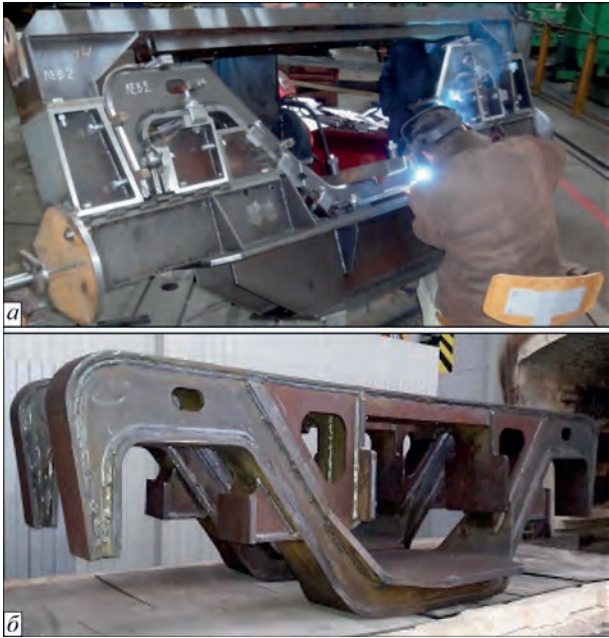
Оснащення для збирання та зварювання конструкції бічної рами (а) і два виготовлених дослідних зразка (б)
